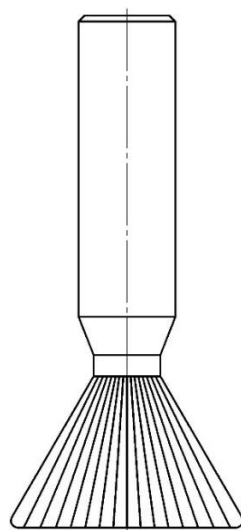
Цільна двокутова фреза для оброблення елементів з'єднання типу "хвіст ластівки" ISO 3859
